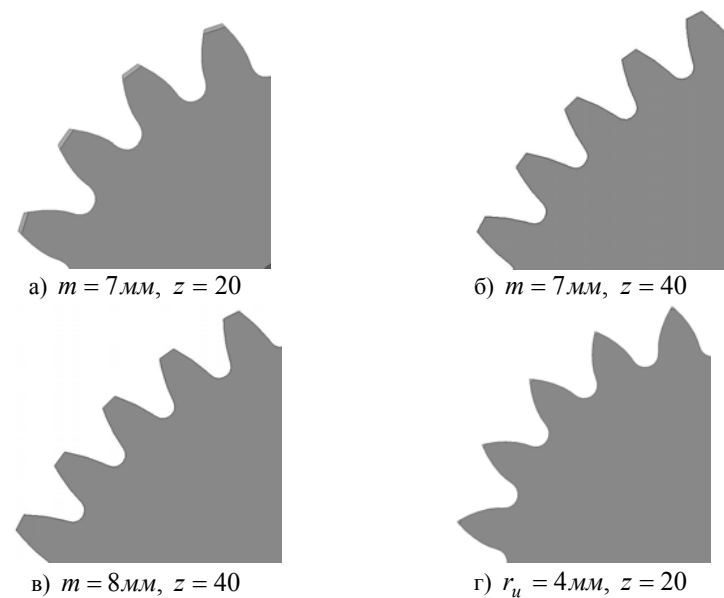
Оброблювальні деталі з періодичним профілями (а, б, в – евольвентні зубчасті колеса; г – цівкове колесо)
